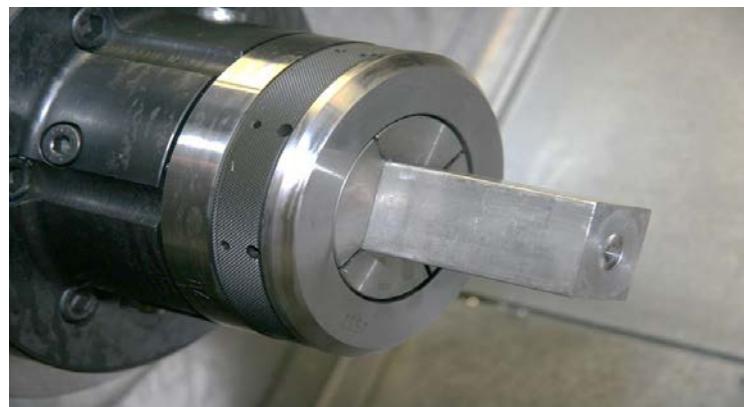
Патрон с цангой для закрепления заготовок с квадратным поперечным сечением
